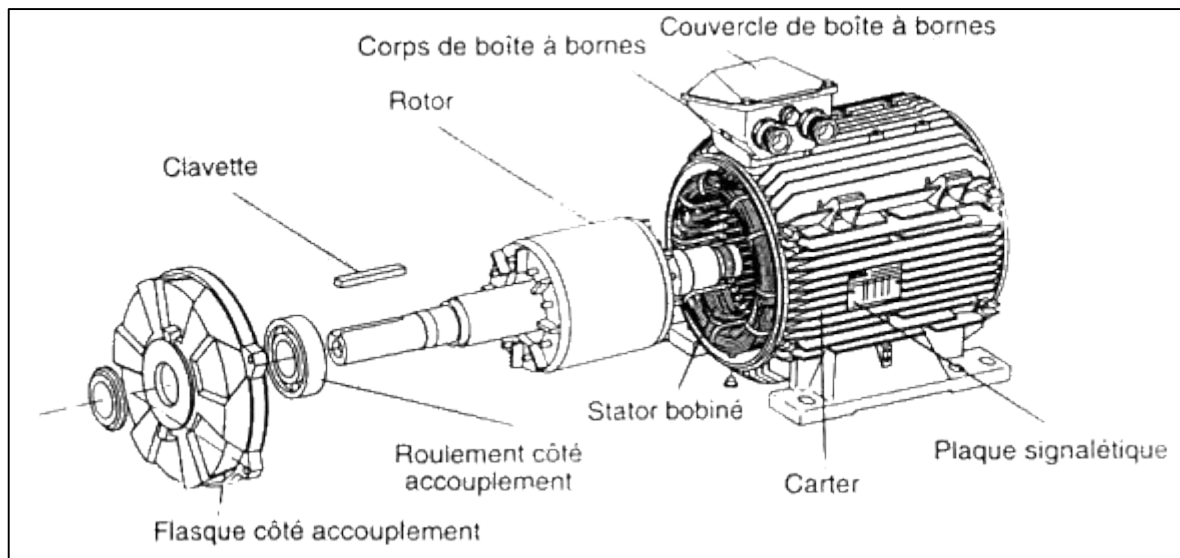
vue éclaté d'une machine asynchrone double étoile
